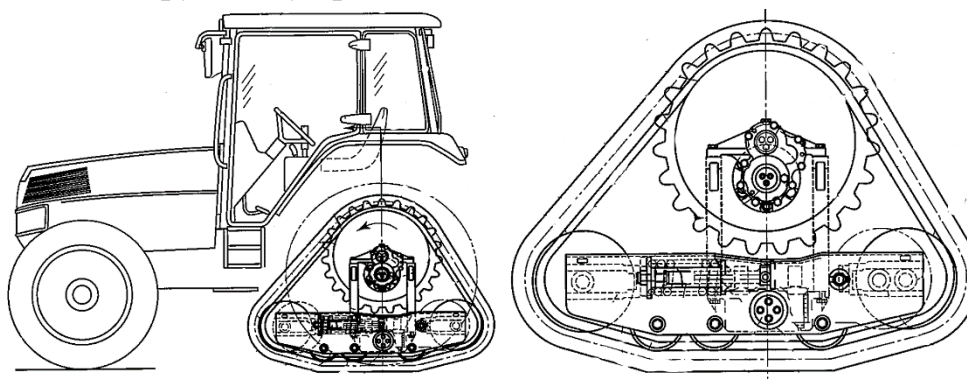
Внешний вид конструкции патента KR 20120102021 A
